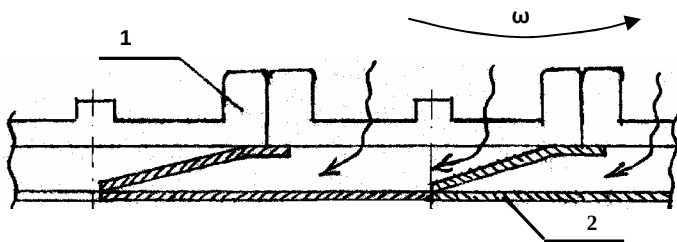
Новая конструкция элеватора: 1 – решетка, 2 – элеватор
